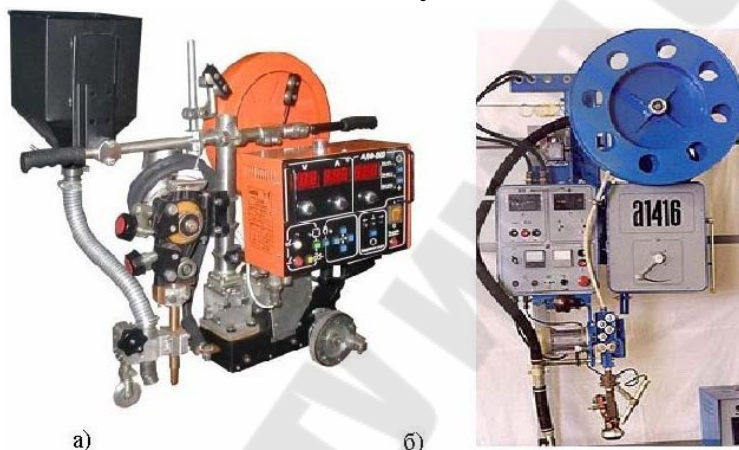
Сварочный трактор АДФ-800 (а) и сварочный автомат А-1416 (б), применяемые для наплавки деталей под слоем флюса
